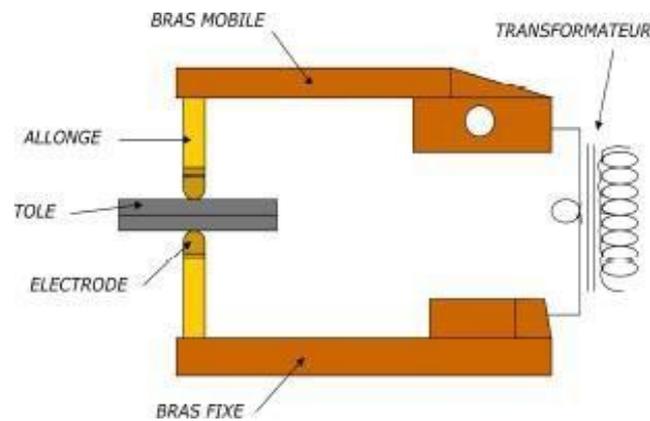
Mécanisme du soudage par point [6].
